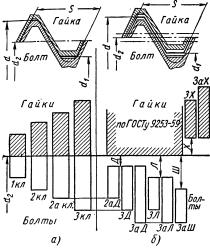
Схемы расположения полей допусков метрической резьбы: a — в скользищих посадках; b — в посадках с зазором
